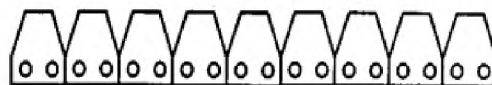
Пристрій для зрізування гички з зворотньо-поступальним рухом ножів
